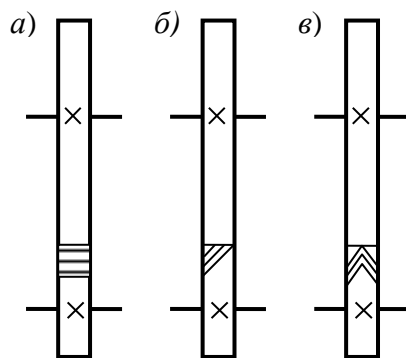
Зубчатые передачи цилиндрическими колесами
